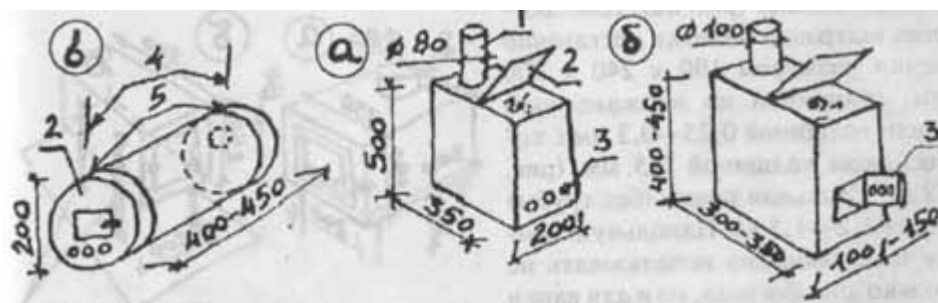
Конструкции печек для обогрева: а), б) неразборные с вертикальной загрузкой дров; в) разборная
